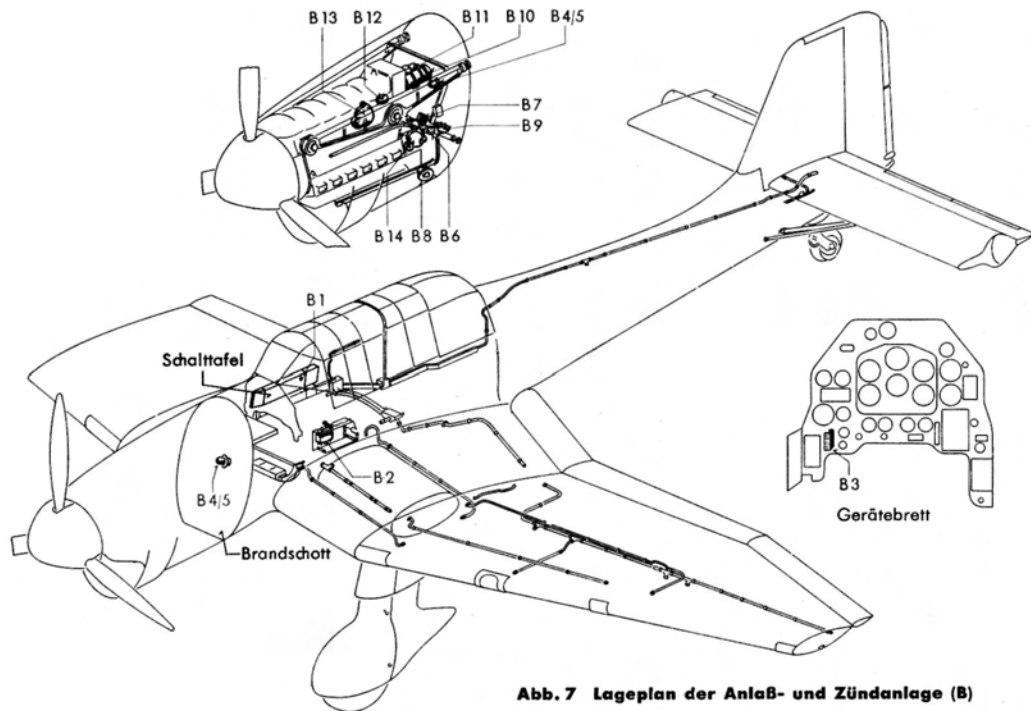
Lageplan der Anlaß- und Zündanlage (B)
